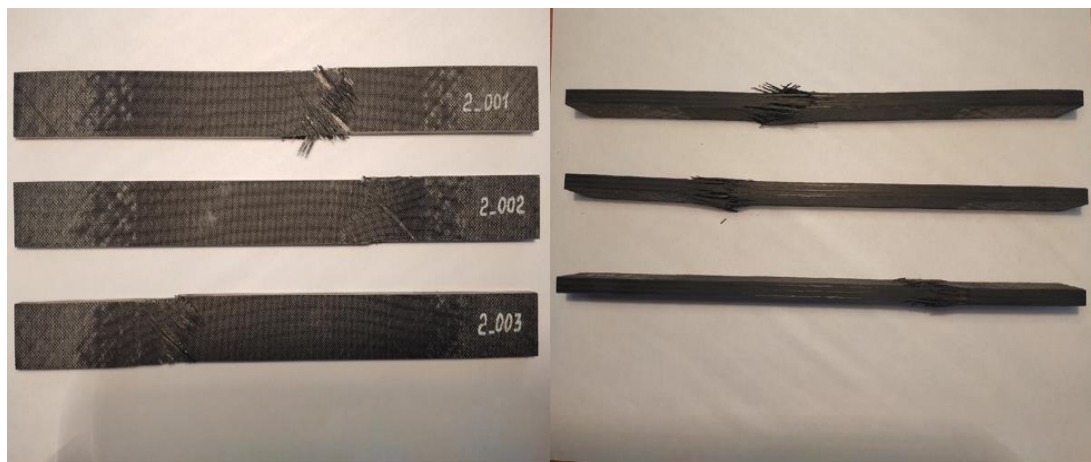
Разрушенные образцы конструкции с наночастицами (ASTM D3039/ГОСТ Р 57745)
